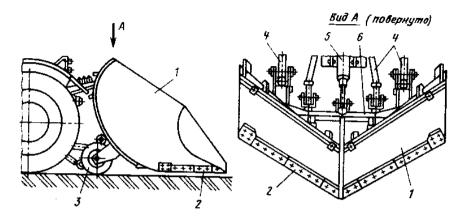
Рабочий орган плужного двухотвального снегоочистителя: 1 – отвальная поверхность; 2 – нож; 3 – опорный ролик; 4 – элементы подвески; 5 – гидроцилиндр подъема рабочего органа; 6 – рама
